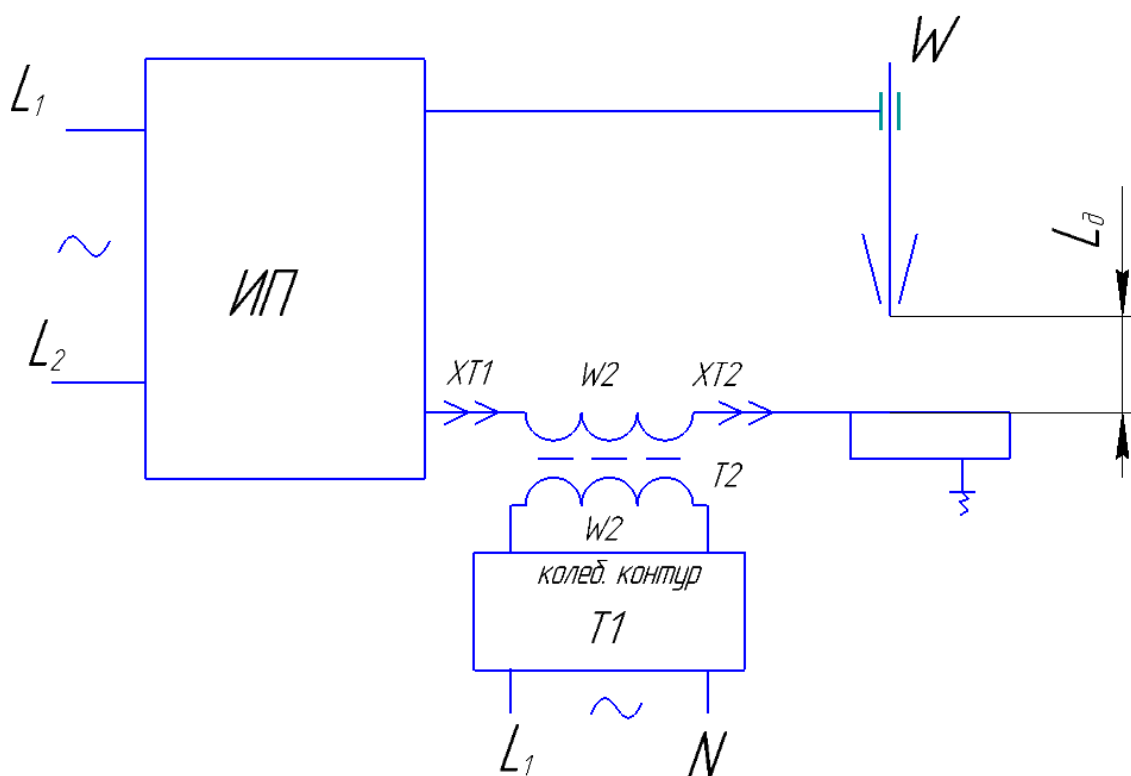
Схема подключения осциллятора в сварочной цепи
